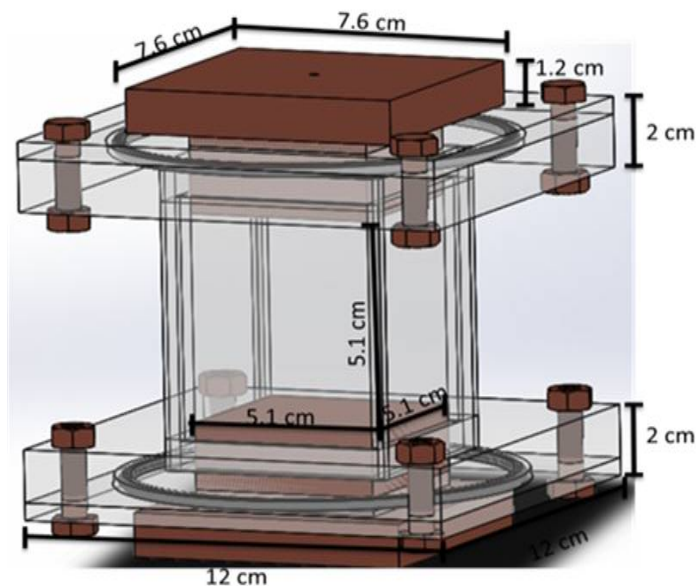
Ensamble completo de la cavidad con dimensiones principales.
